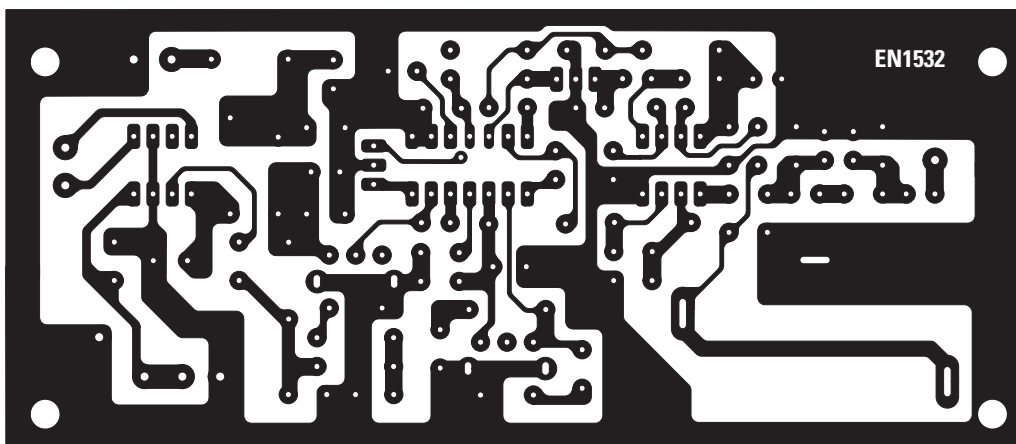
2: Dessin, à l'échelle 1, du côté soudures du circuit imprimé double face à trous métallisés.
